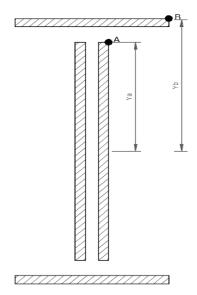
Perfil IPN200 y filetes de soldadura
